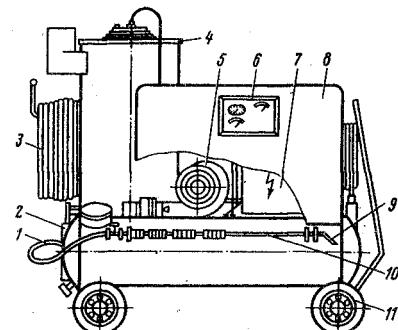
Передвижной пароводоструйный очиститель ОМ-3360А:
